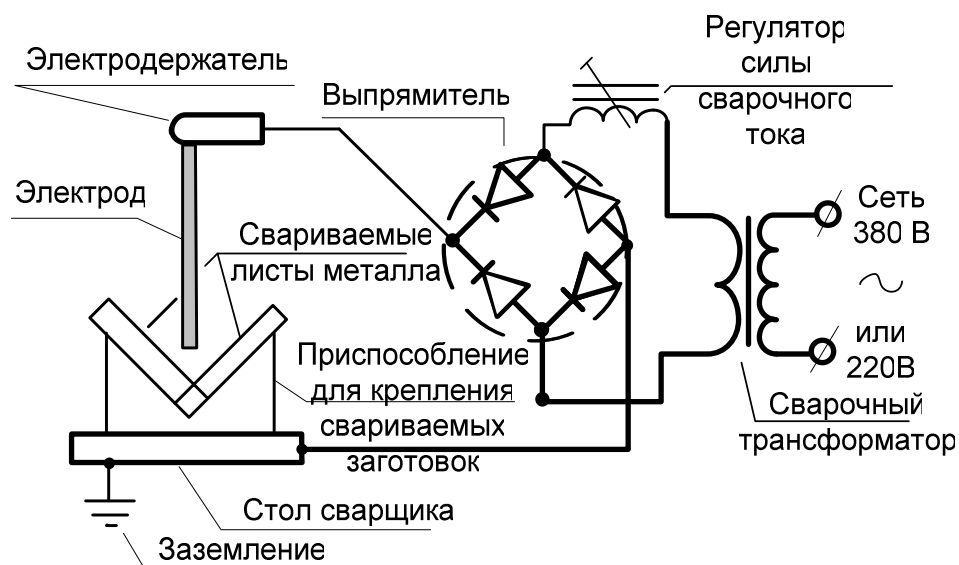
Принципиальная схема сварки выпрямленным током
